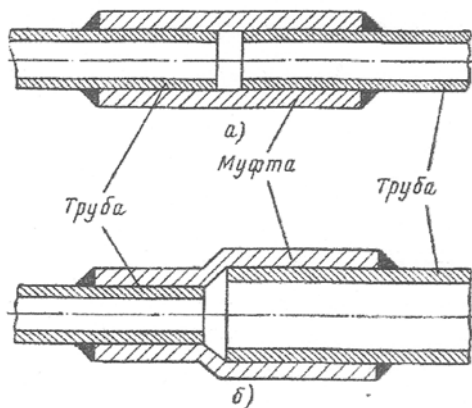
Схемы стыковки труб [1]: а) одинакового; б) разного диаметров. 1 - трубы; 2 - герметизирующие галтели, образованные сваркой или пайкой
